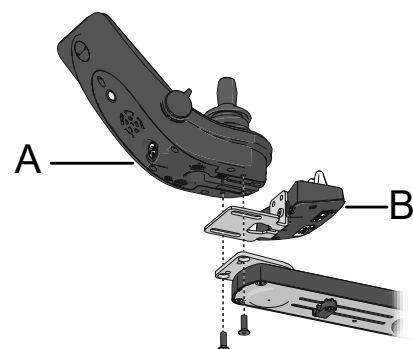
Das Steuerpult ist mit zwei Schrauben auf dem parallelen Pulthalter befestigt.
